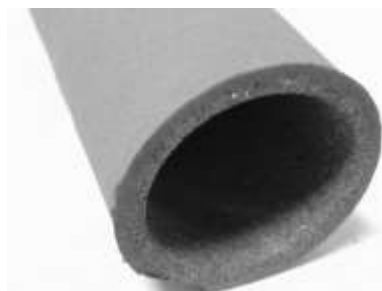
Деталь конструкційного призначення (пористий матеріал)
